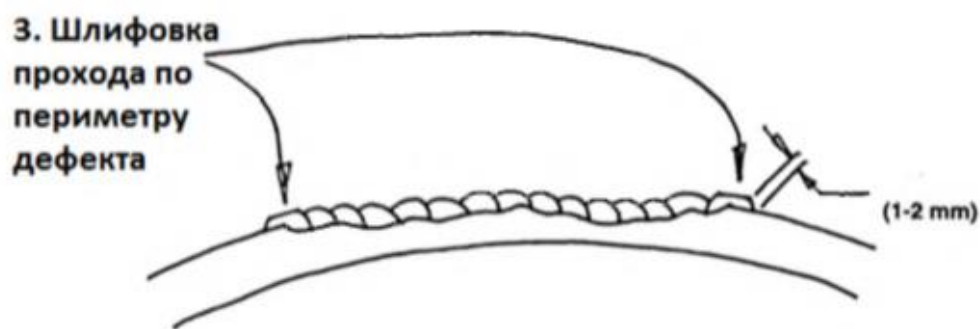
Схема шлифовки сварочного прохода по периметру
